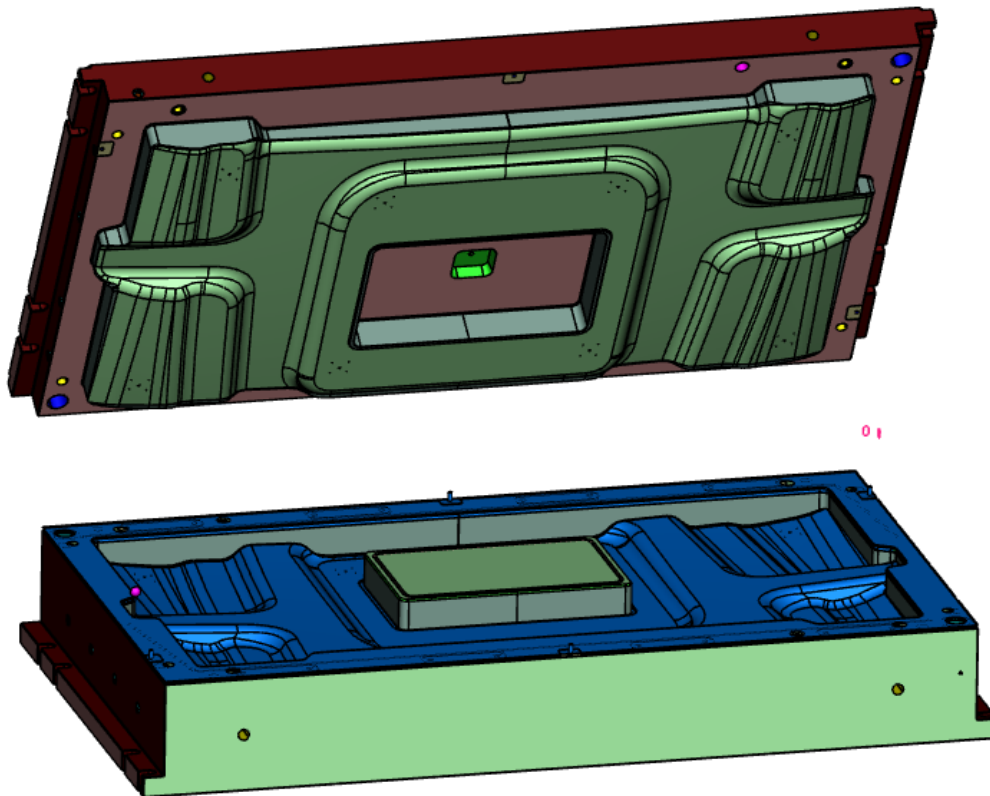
CAD-Daten des Schaumkernwerkzeuges für die Dachfläche
